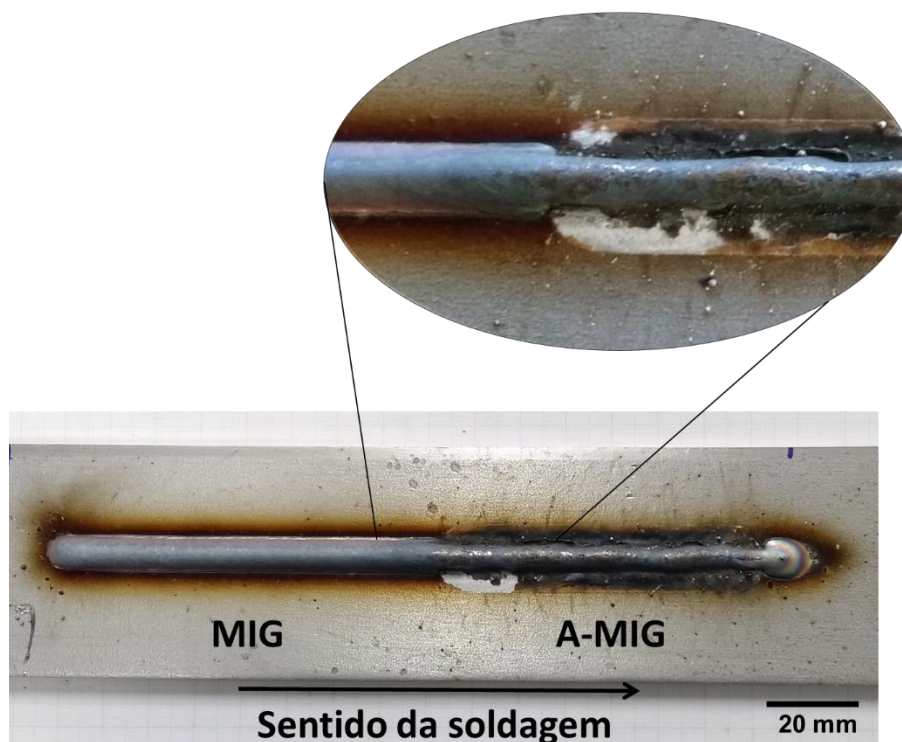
Cordão de uma soldagem A-MIG com  $\text{SiO}_2$  como fluxo e detalhe exibindo diferença no aspecto do cordão na soldagem A-MIG e MIG.
